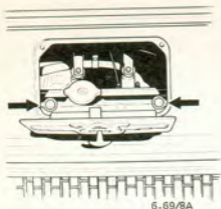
Voorraadtankje van hydraulisch bediende koppeling
